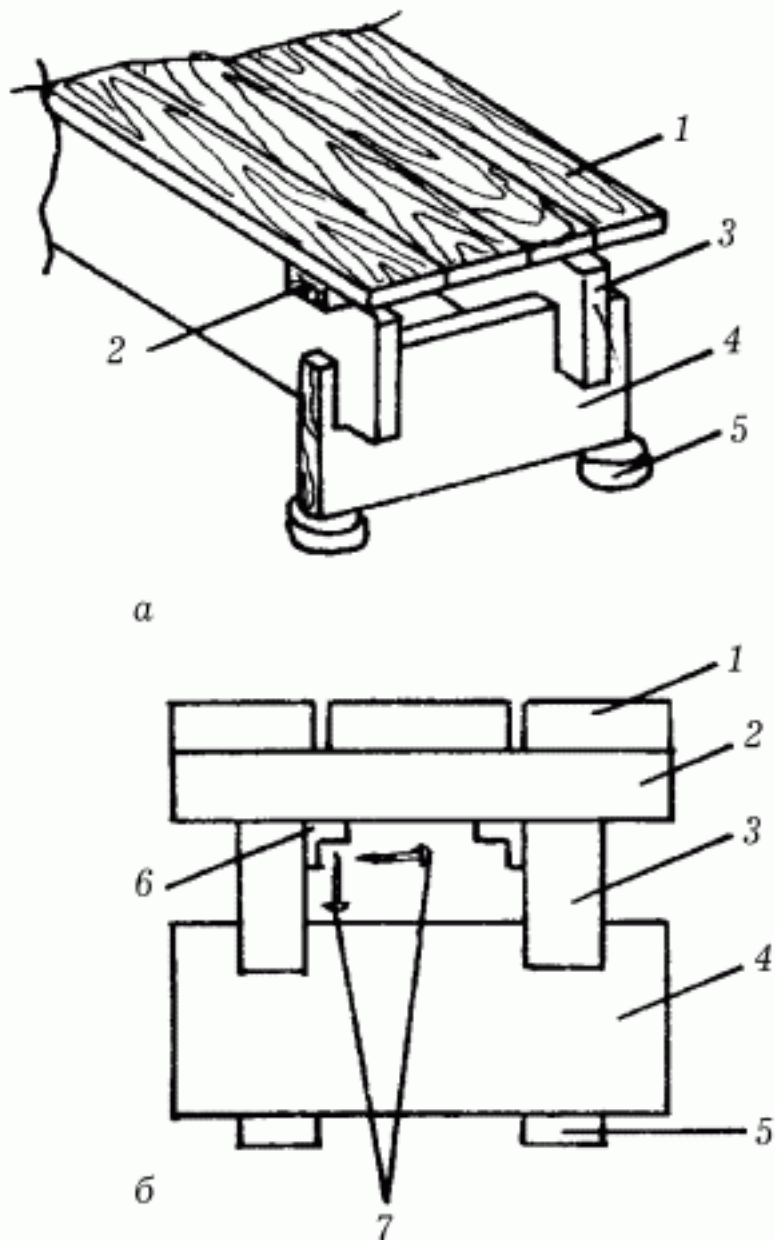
Скамейка-лежанка: а – общий вид; б – схема крепления щита к раме; 1 – доски; 2 – опорный брусок; 3 – рамный брусок; 4 – опора; 5 – резиновая подножка; 6 – мебельный уголок; 7 – шурупы.
